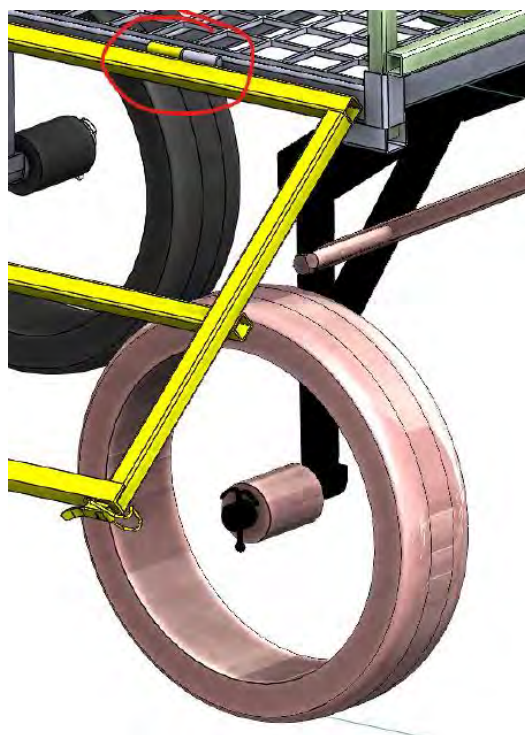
Vue de détail du porte-tout-petit : les ridelles sont sur pivot
